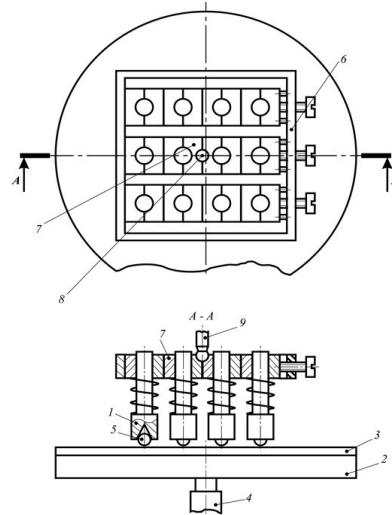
Устройство для полирования заготовок шаровидной формы
